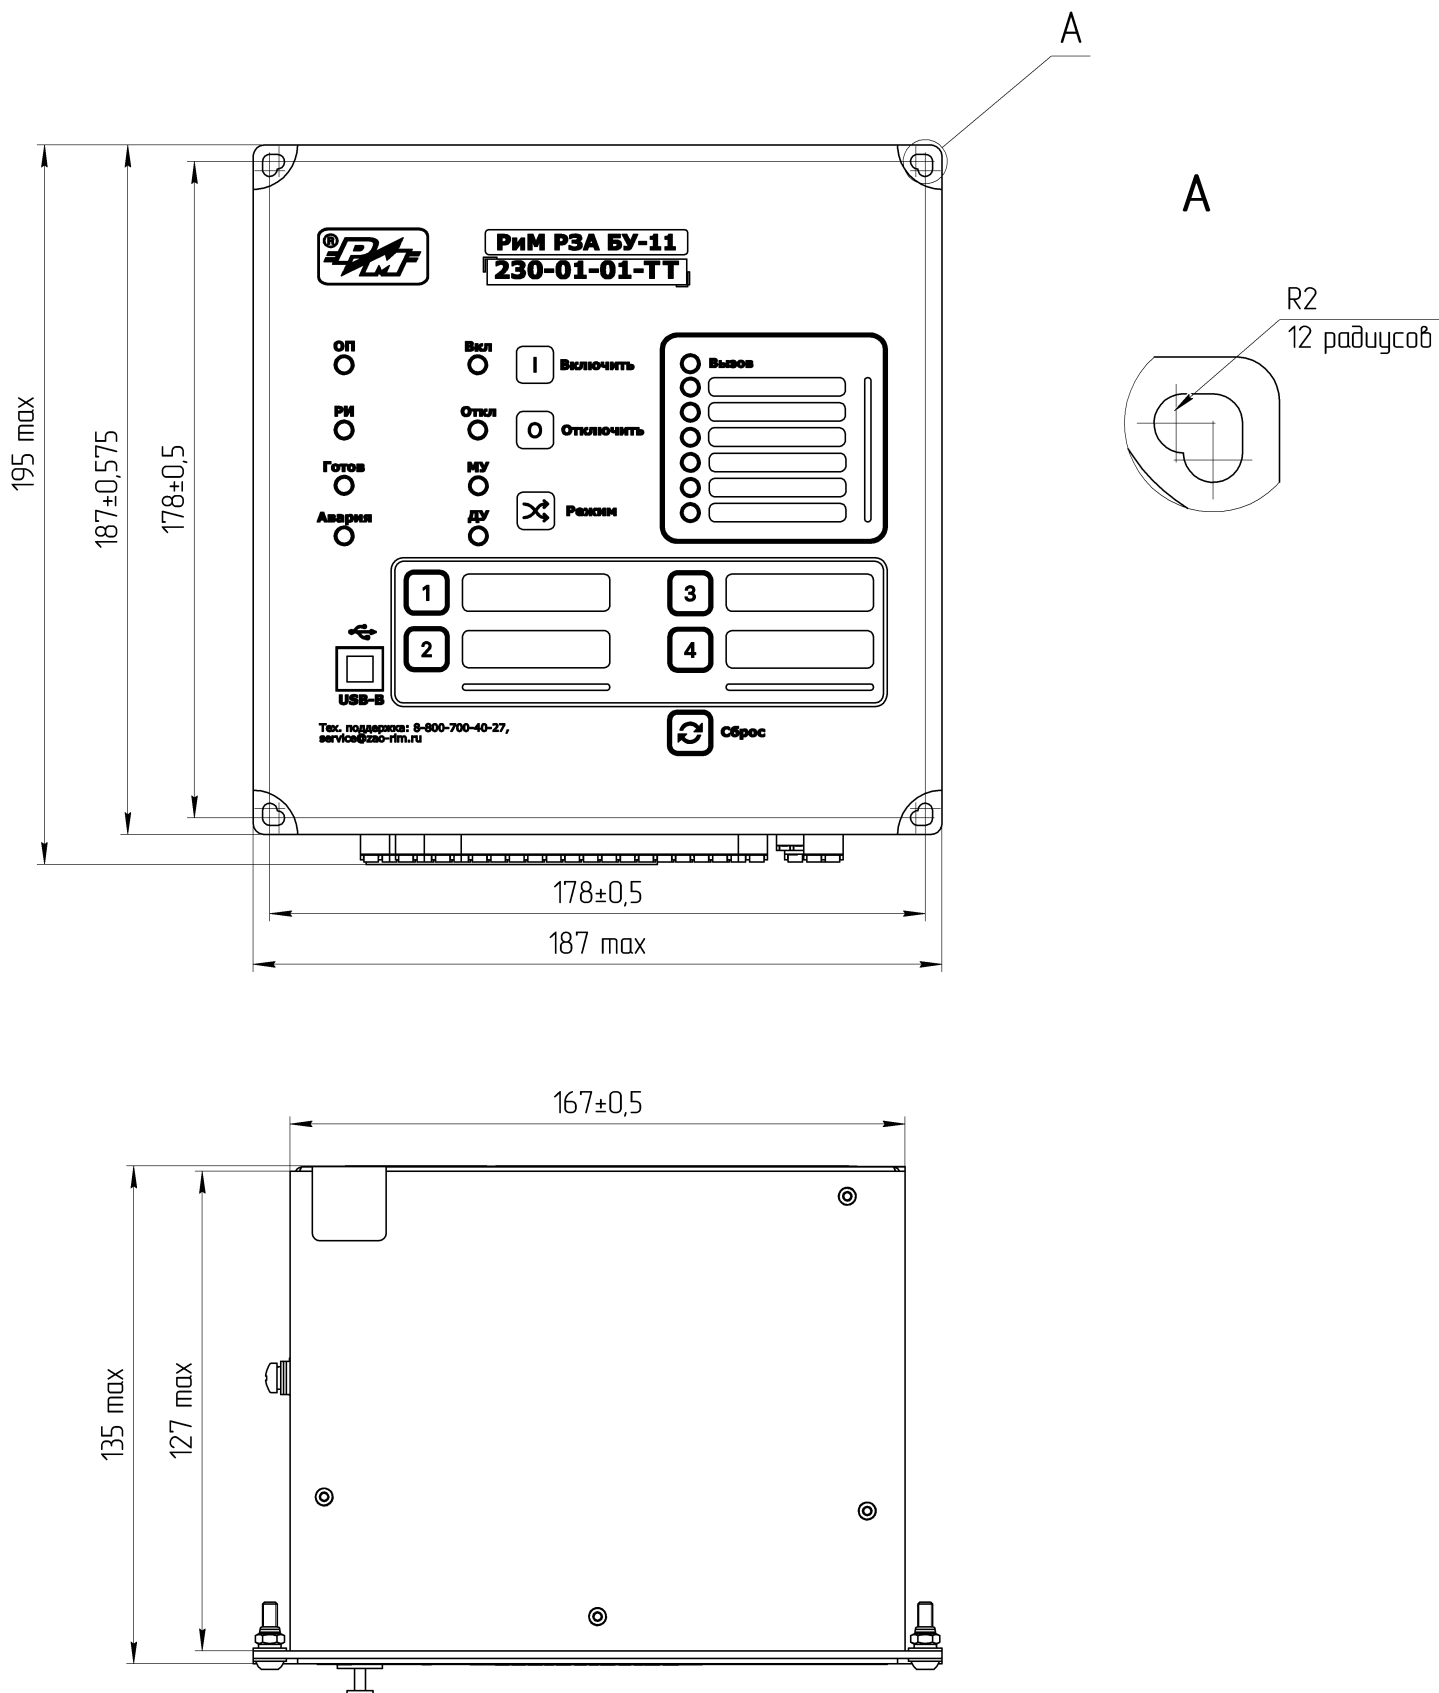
Габаритные и установочные размеры устройств РЗА
